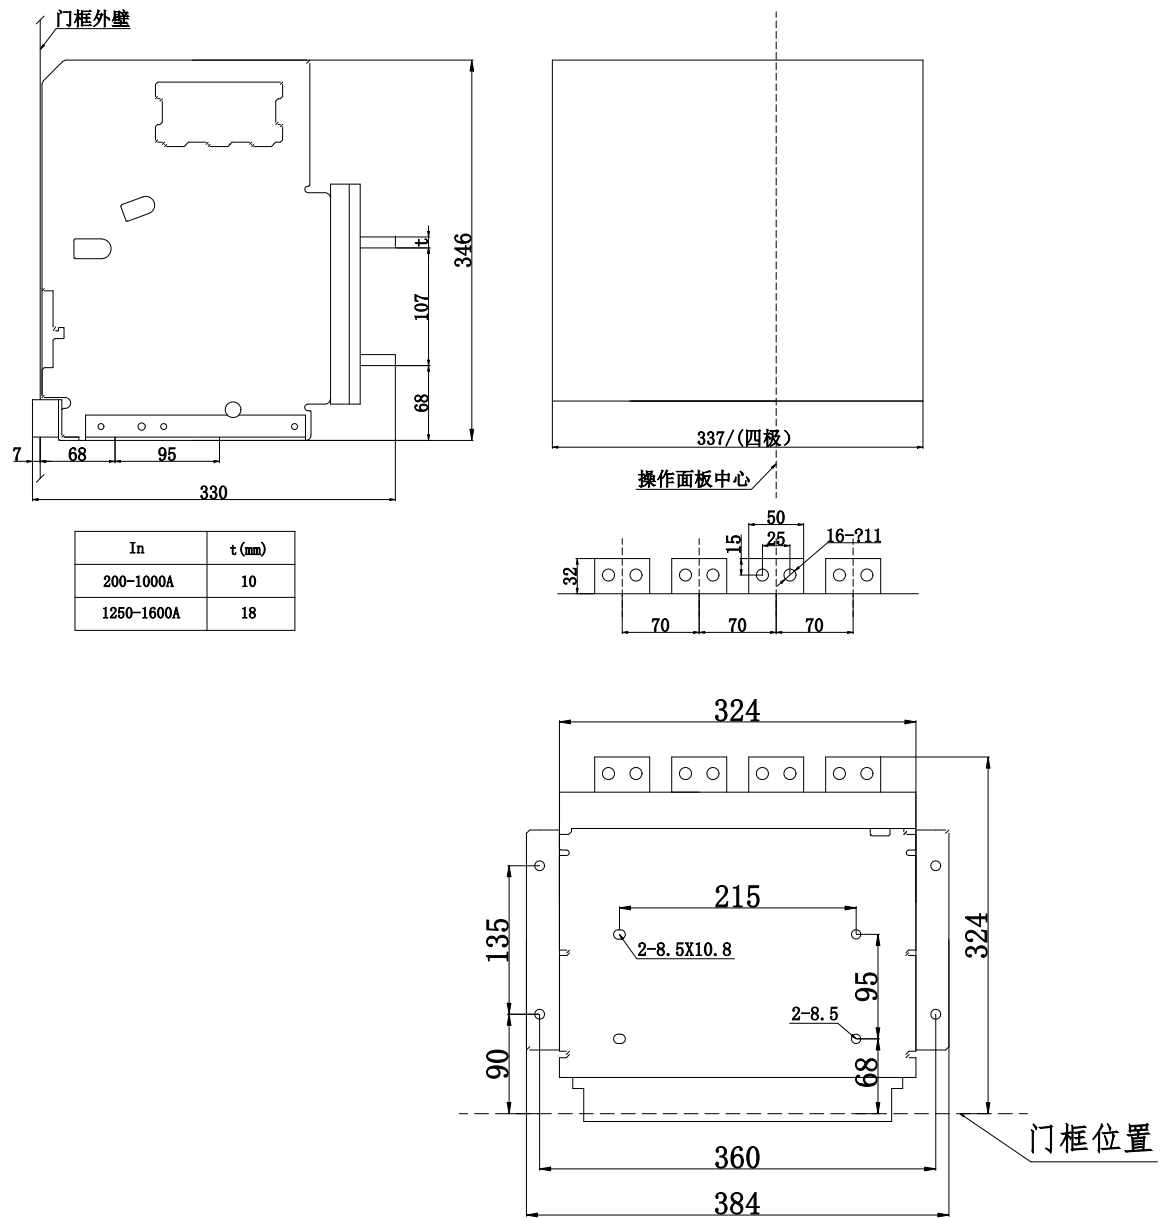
抽屉式断路器 4P 外形及安装尺寸
